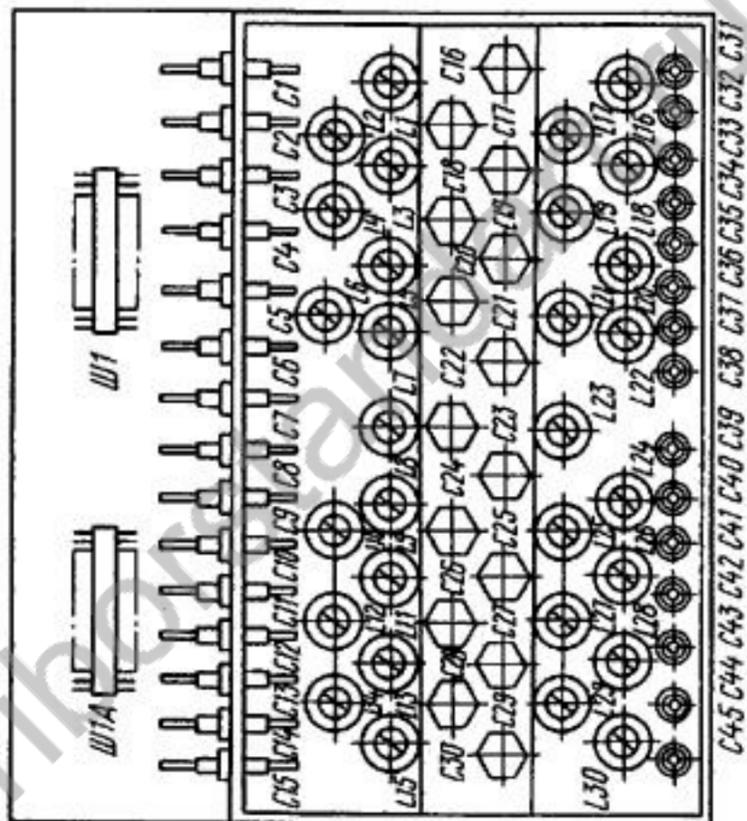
Устройство соединительное 5.282.225, план размещения элементов
